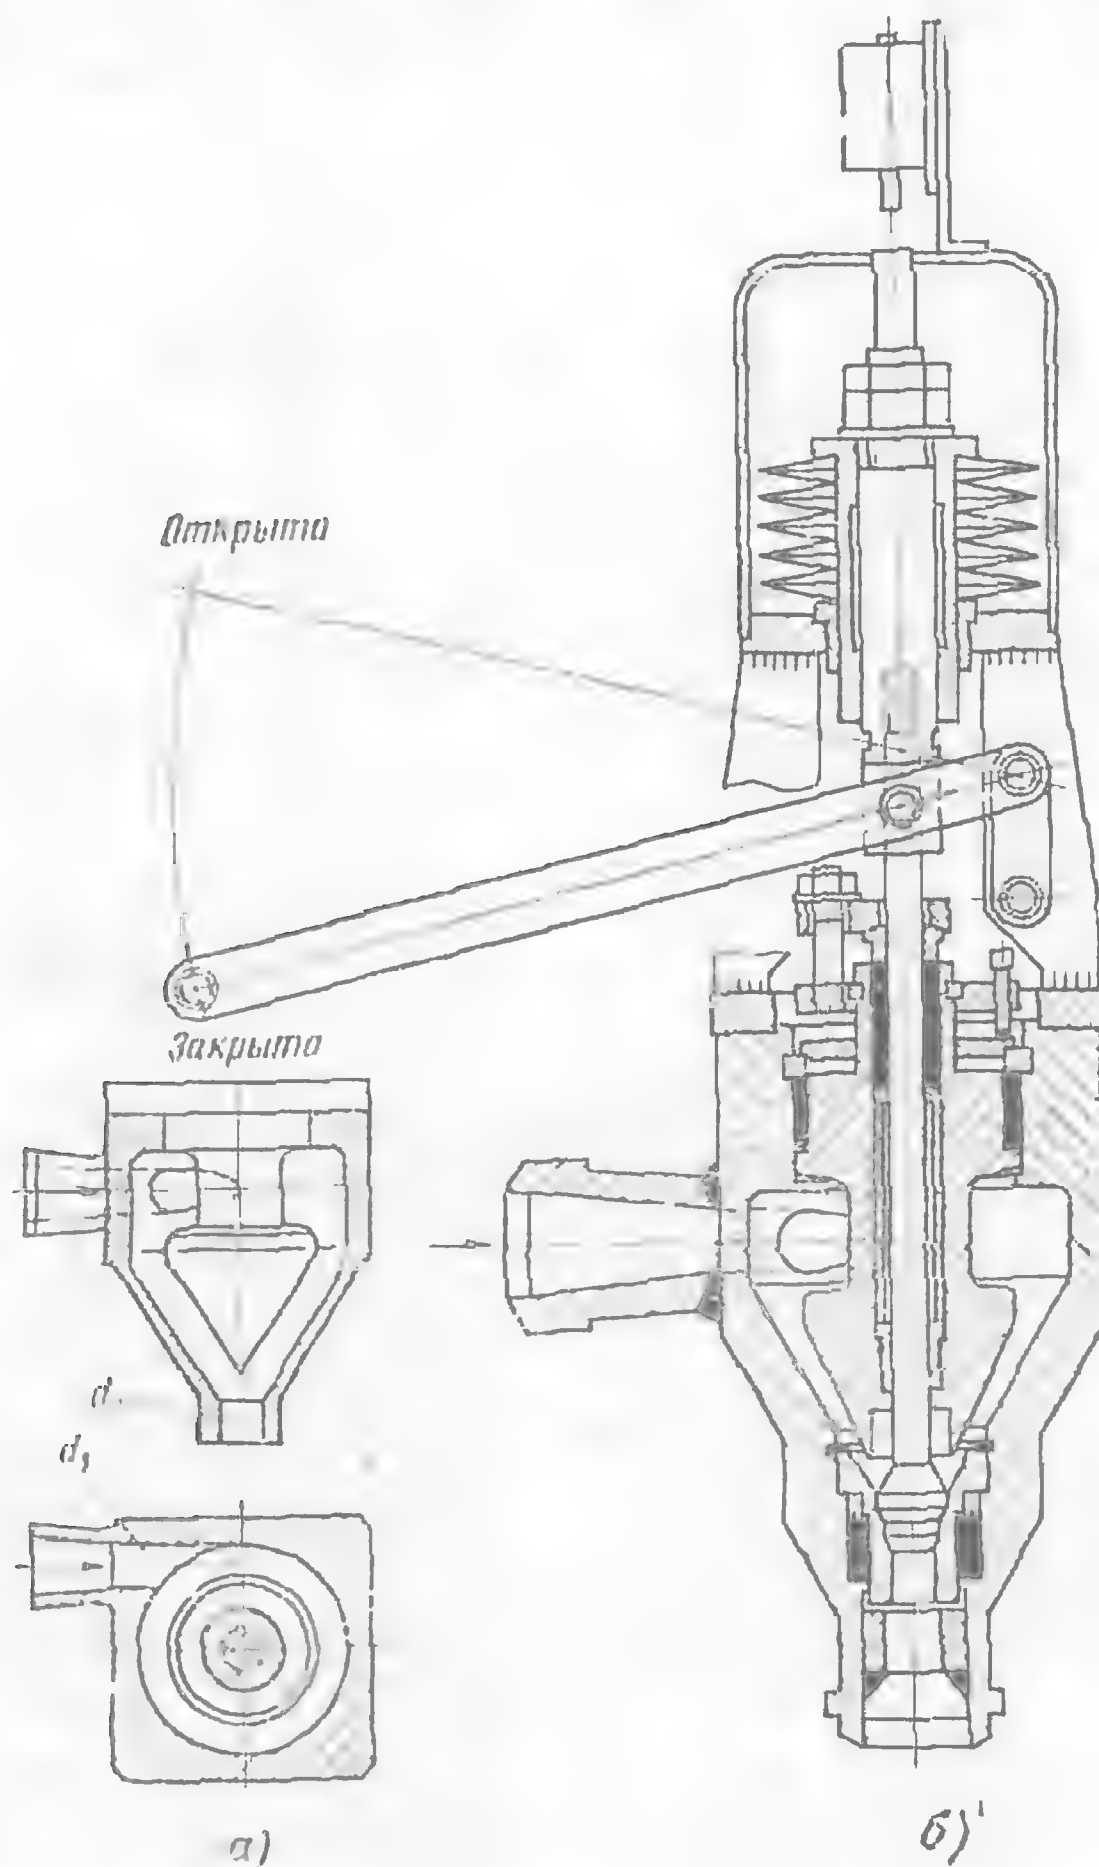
Клапан центробежного типа конструкции фирмы Панконтроль (ФРГ).
